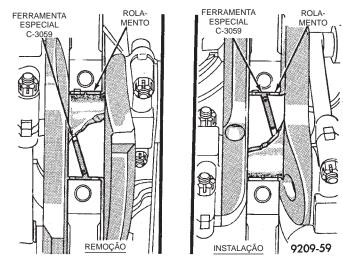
Remoção e Instalação do Rolamento Principal Superior com a Ferramenta C-3059
